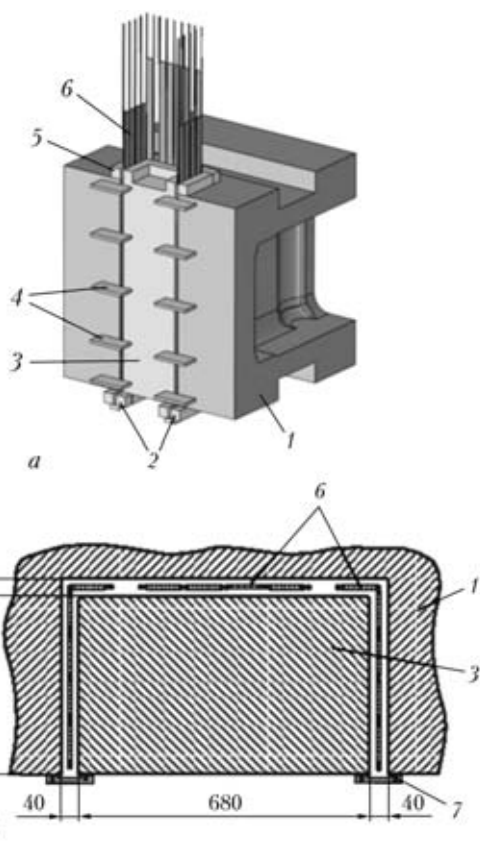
Общий вид (а) и схема сборки под ЭШС плавящимся мундштуком (б): 1 — свариваемое изделие; 2 — входные карманы; 3 — кованая вставка (имплантат); 4 — технологические планки; 5 — выходные карманы; 6 — плавящиеся мундштуки; 7 — формирующие устройства
